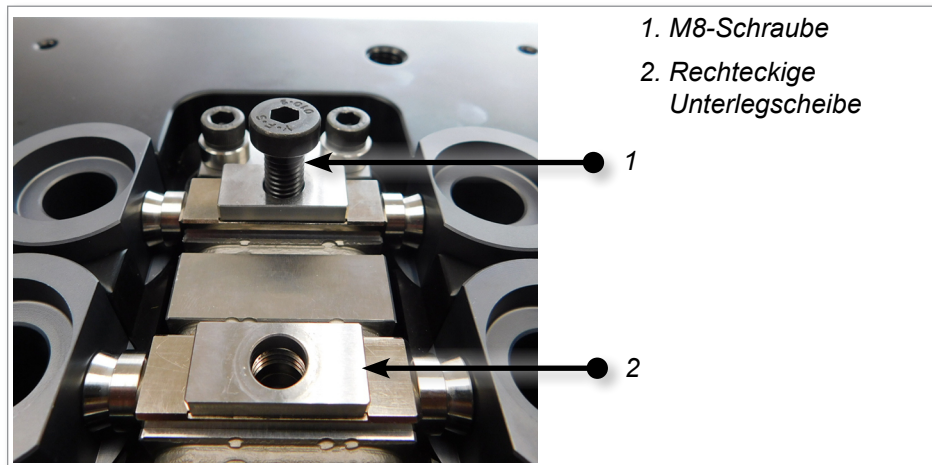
Installation der rechteckigen Unterlegscheiben und der Schrauben
